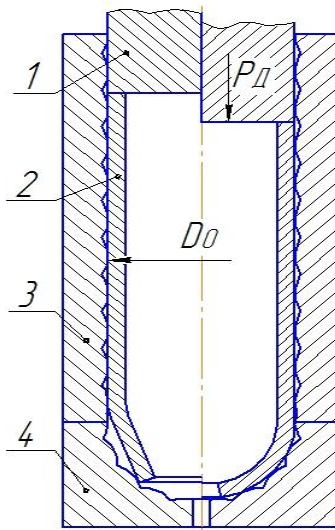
Схема закрытого обтиску трубчатой заготовки в спрофилированной матрице
